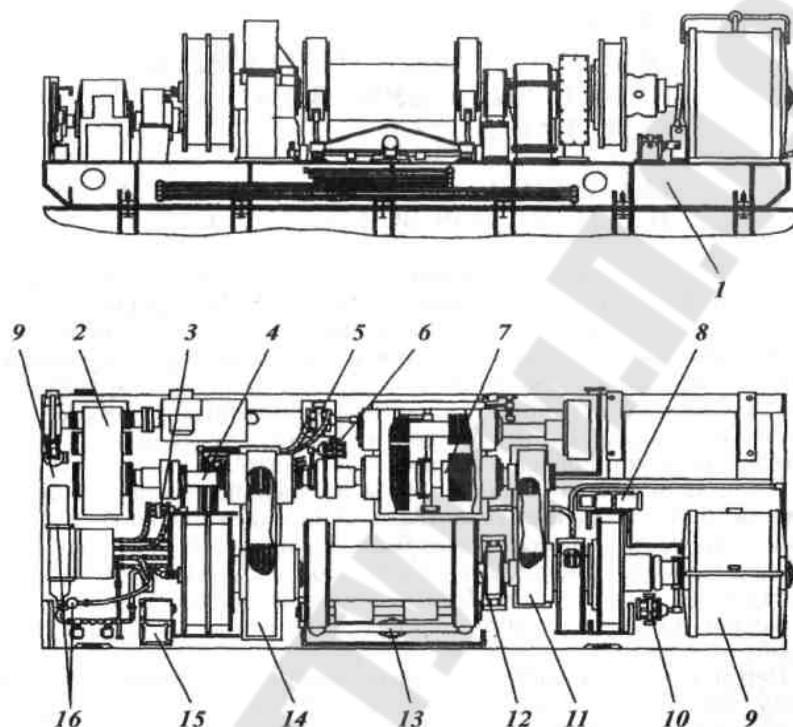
Лебедка буровая типа ЛБУ: 1 - рама; 2 - регулятор подачи долота; 3, 10 - механизм включения; 4 - тихоходный вал; 5 - механизм переключения скоростей; 6 - механизм включения зубчатой муфты; 7 - коробка передач; 8 - насосный агрегат системы смазки; 9 -электромагнитный тормоз; 11, 14 - быстроходная и тихоходная передачи; 12 -подъемный вал; 13 - узлы ленточного тормоза; 15 -командоаппарат с датчиком глубины; 16 - воздухопровод
